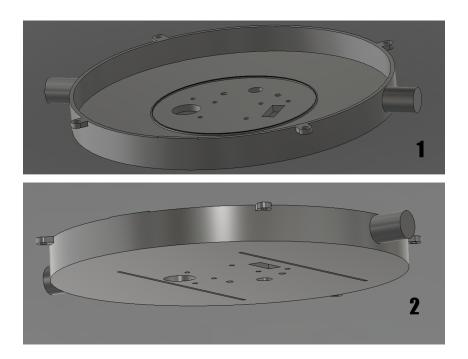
Lower Body. 1 view from above. 2 view from below
